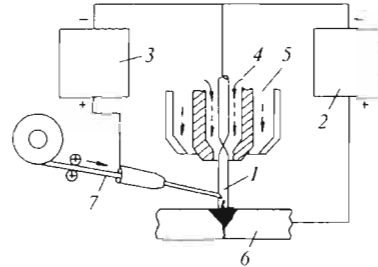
Схема процесса сварки двойной плазменной дугой с токоведущей присадочной проволокой:
